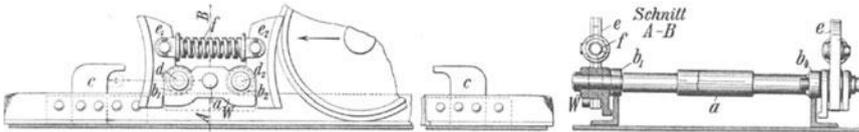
Rollen-Hemmvorrichtung mit Federung.
